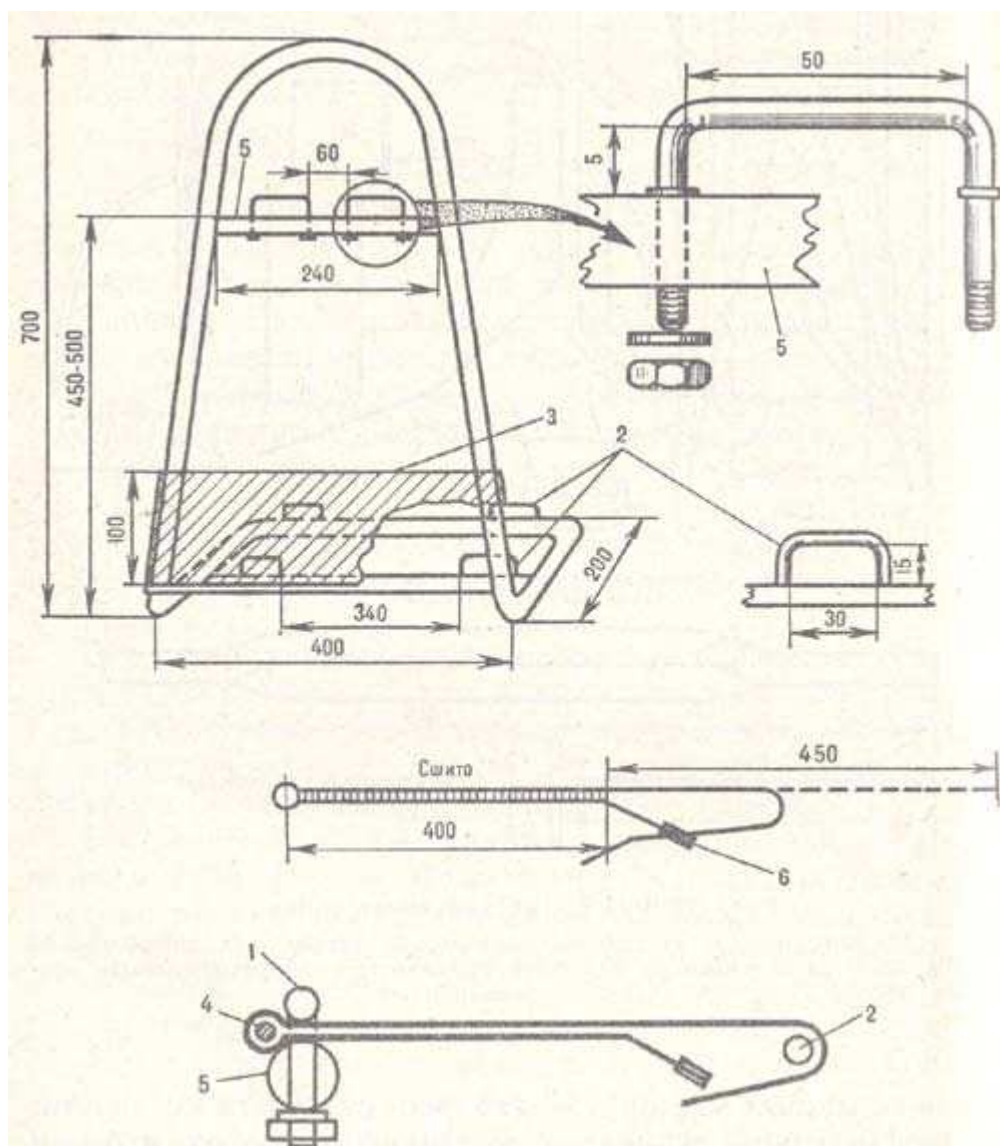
Станок к универсальному рюкзаку (вверху) и плечевые ремни, позволяющие использовать станок без рюкзака: 1 и 2—скобы; 3—опорный пояс; 4—палка (веревка); 5—перекладина; 6 — пряжка.
